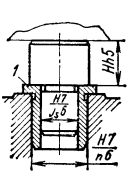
Схемы установки заготовок плоскими поверхностями на:
